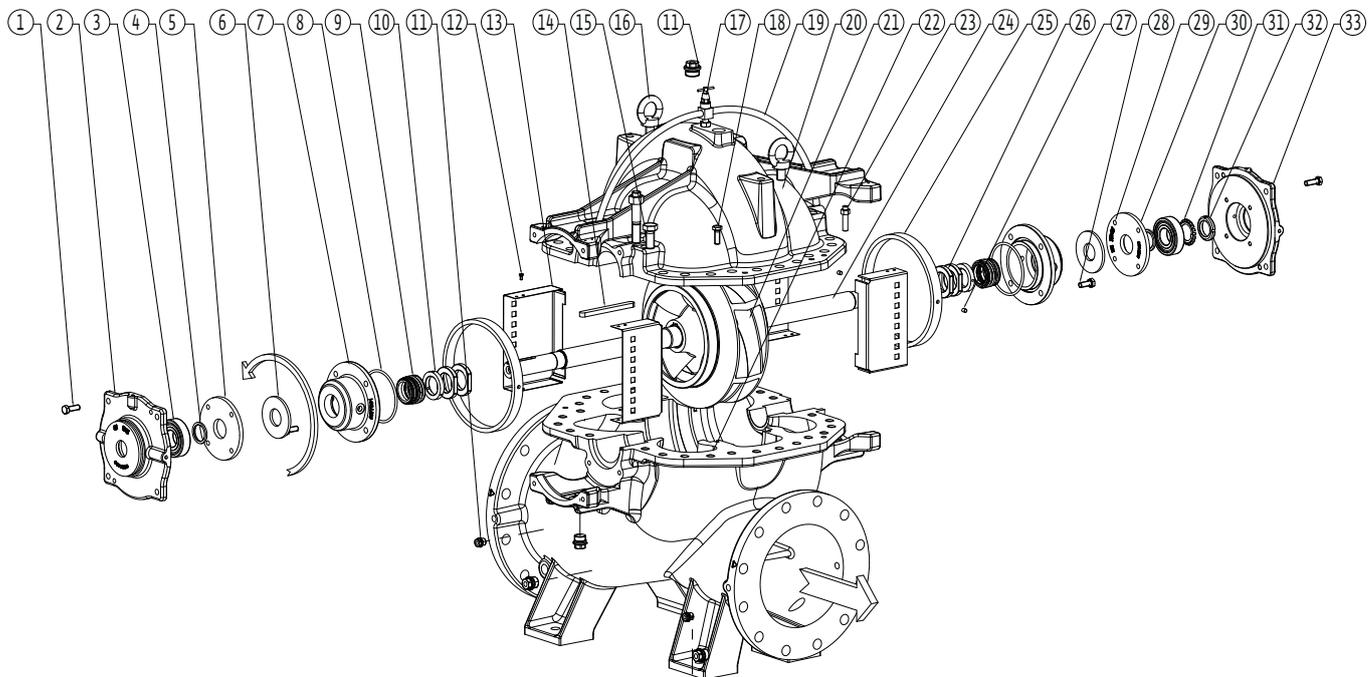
Explosionsansicht der Atmos TERA-SCH-Hydraulik (Ausführung mit Gleitringdichtung ohne Hülsen)
